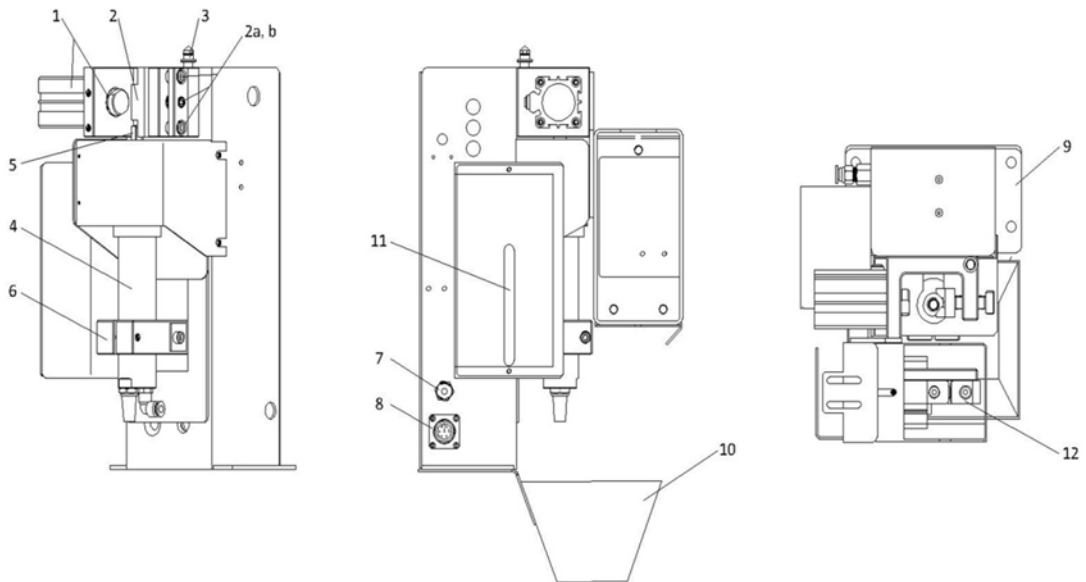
Основные компоненты станции автоматической очистки сварочной горелки
